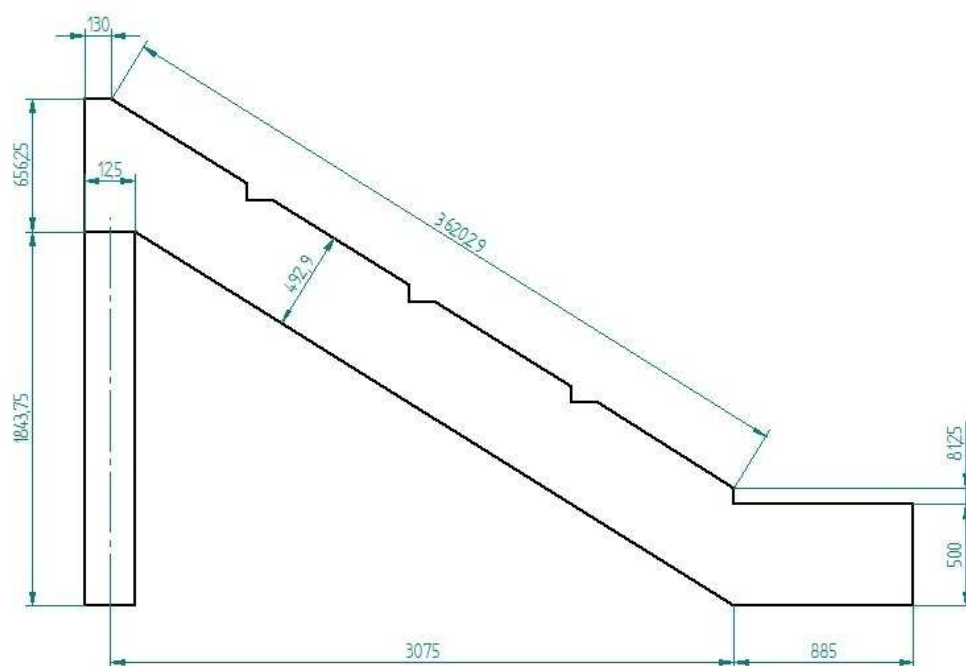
Pórtico de entrada predimensionado (dimensiones en mm)
